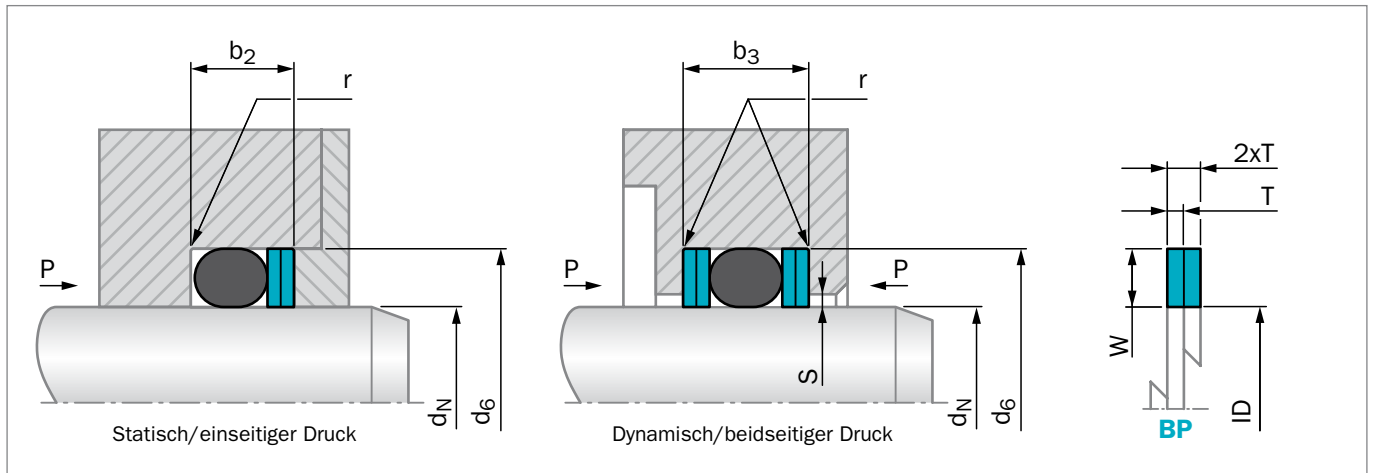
Einbauzeichnung innendichtend, spiralförmiger Stützring-Typ
